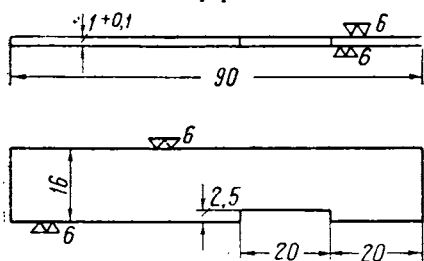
Шаблон для проверки высоты зубьев грейфера, выступающих за поверхность фильмового канала
